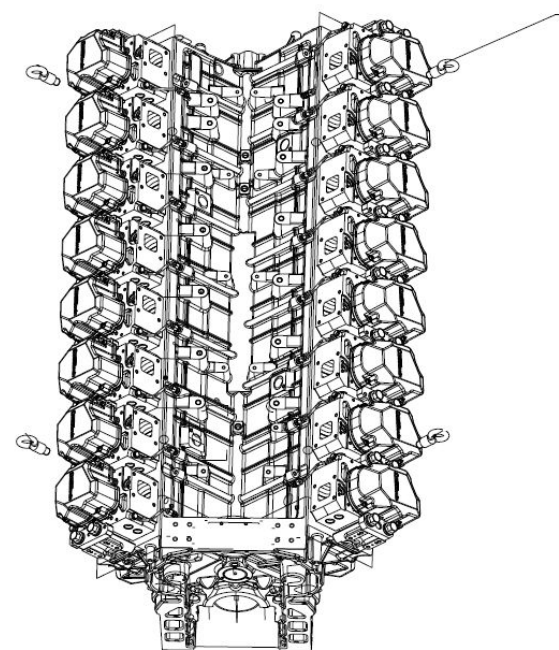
Сборочный чертеж подъемного кольца 16М33
